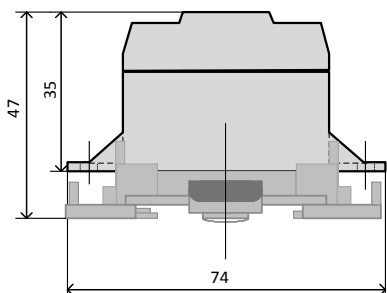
Габаритные размеры устройства для монтажа на рейку DIN.
